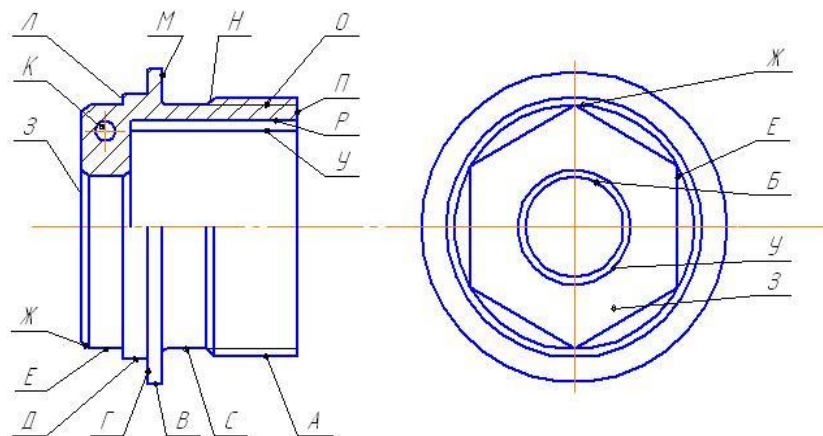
Креслення деталі гніздо пробки 3170707009
